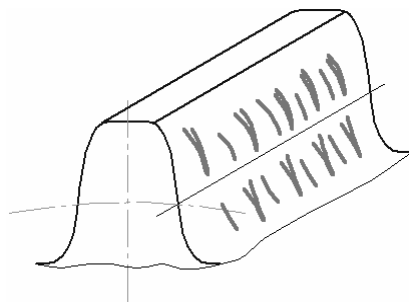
Сліди заїдання на робочій поверхні зуба
